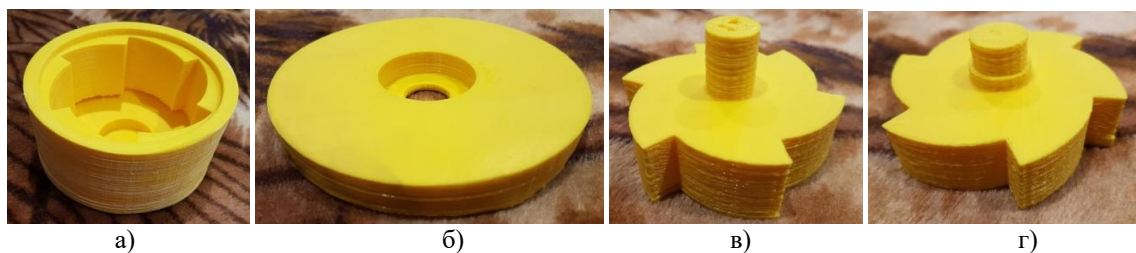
Внешний вид деталей двигателя: а – корпус; б – крышка корпуса; в – верхняя часть ротора; г – нижняя часть ротора.
